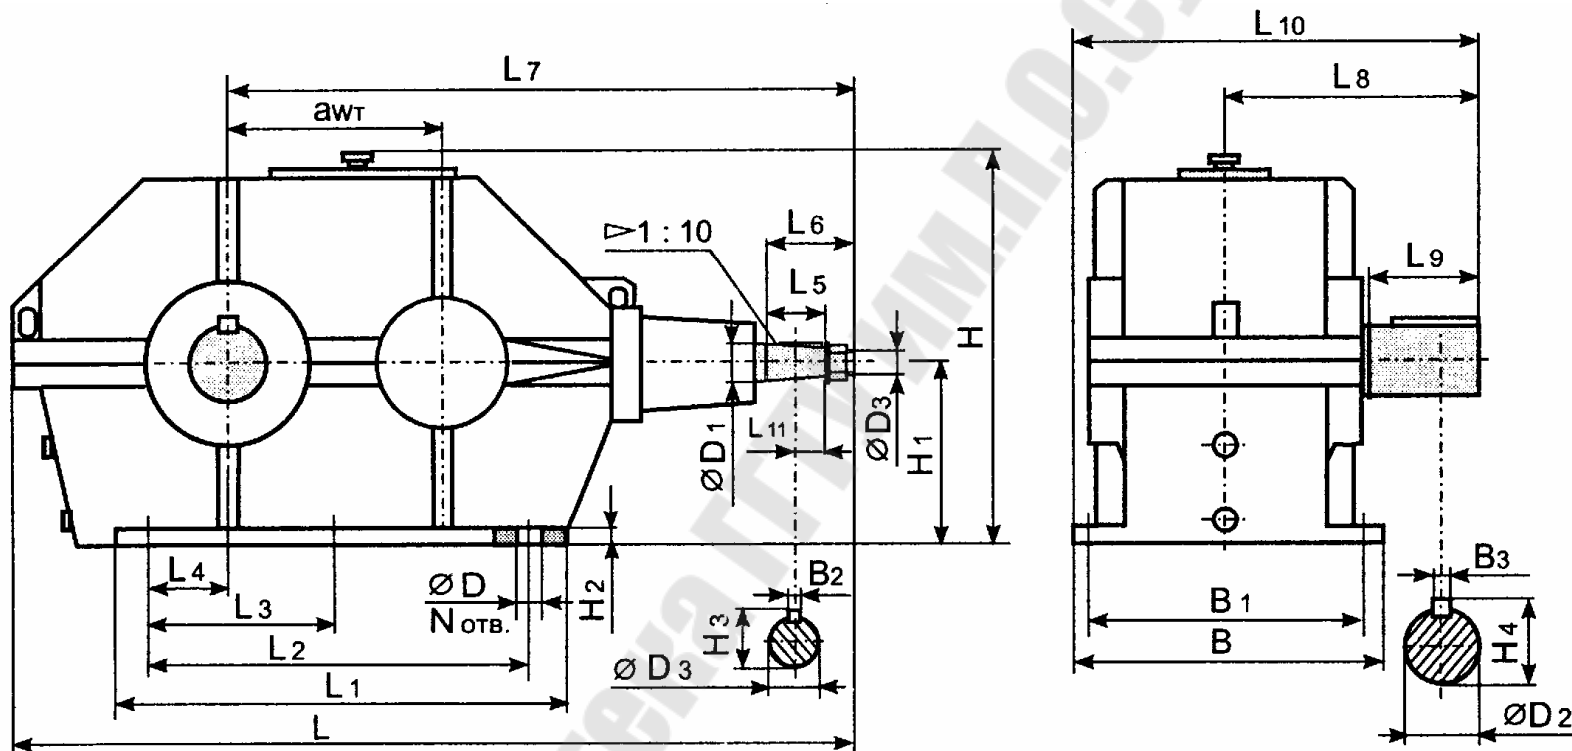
Редуктор коническо – цилиндрический двухступенчатый
